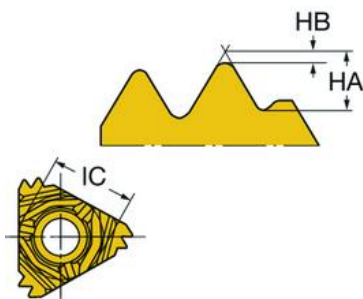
Державка різця «266RFG-2525-22»
